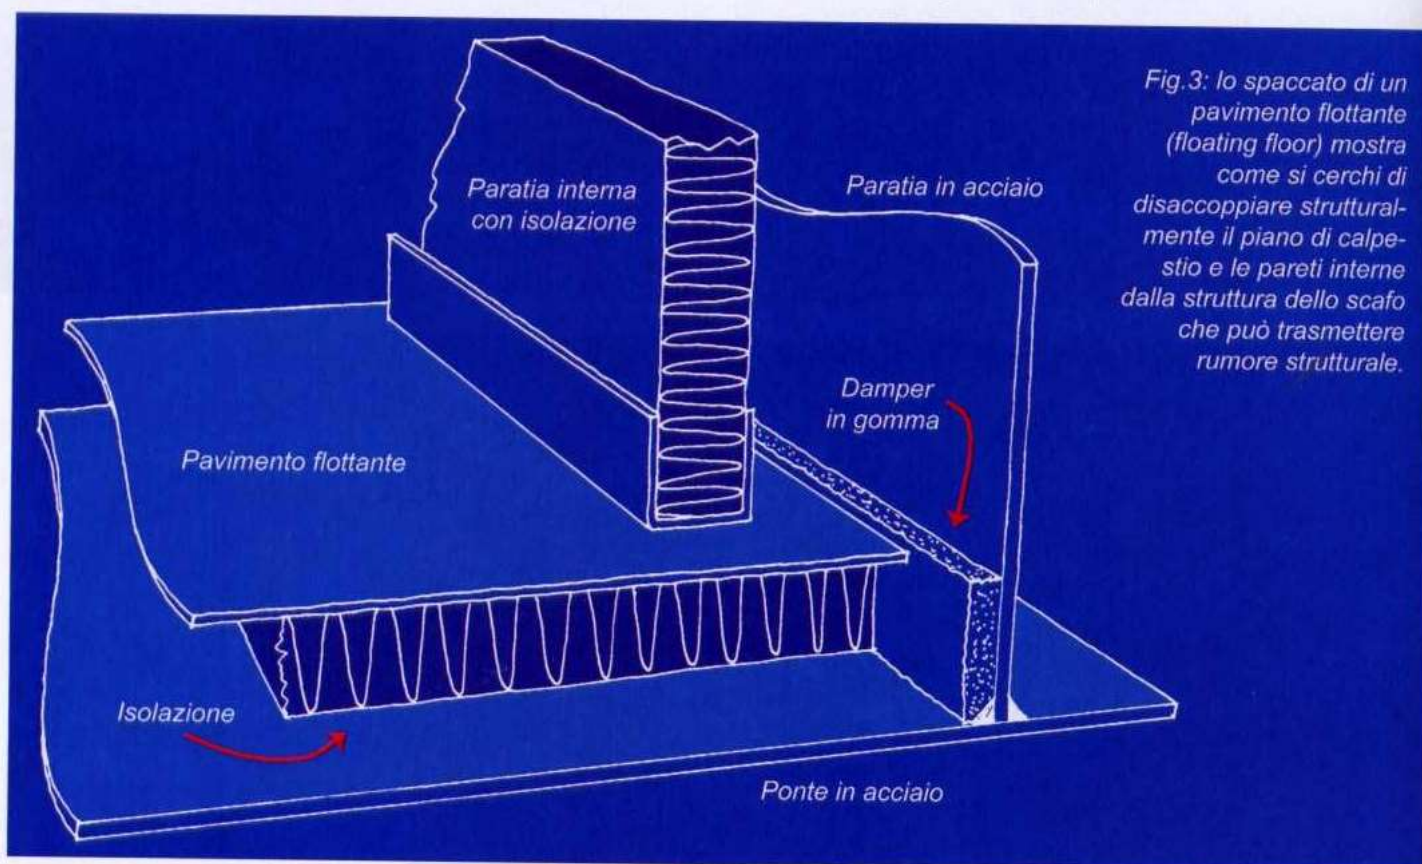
lo spaccato di un pavimento flottante (floating floor) mostra come si cerchi di disaccoppiare strutturalmente il piano di calpestio e le pareti interne dalla struttura dello scafo che può trasmettere rumore strutturale.
